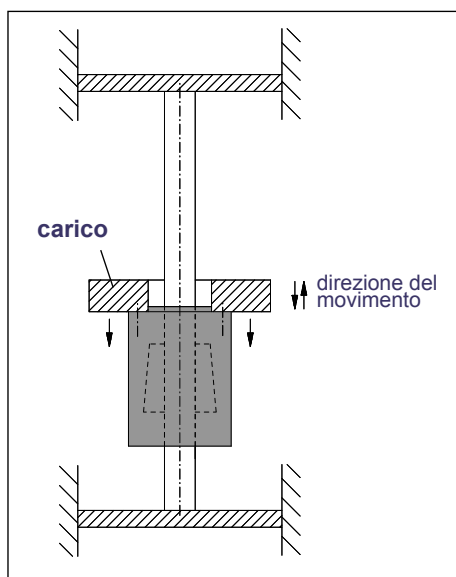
Fissaggio del dispositivo bloccastelo traslante
